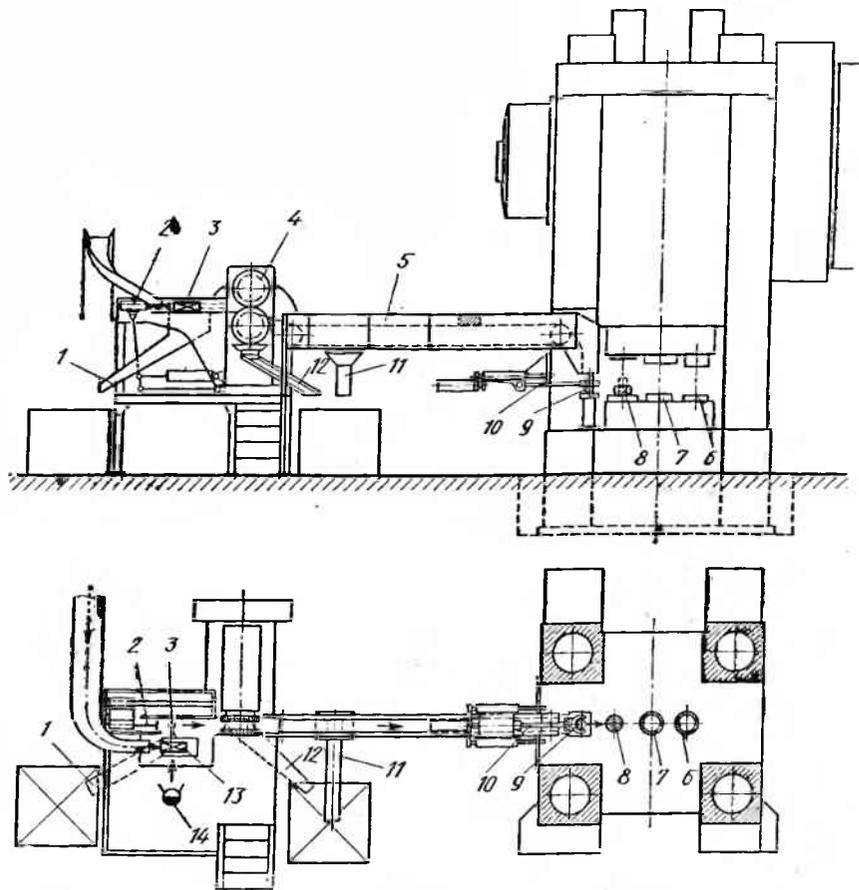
Схема механизированной штамповки на кривошипном горячештамповочном прессе
